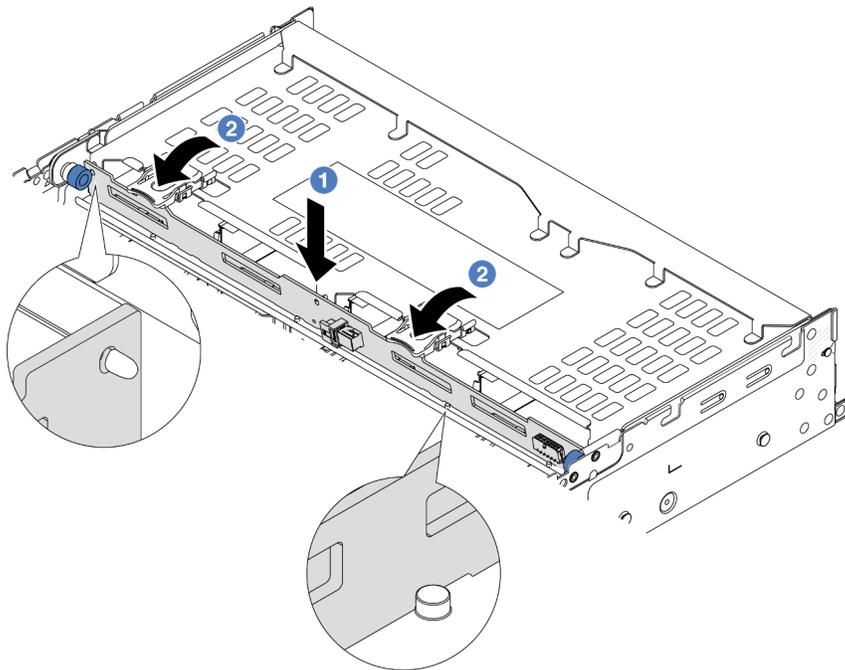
Installation du fond de panier d'unité 4 x 3,5 pouces arrière
